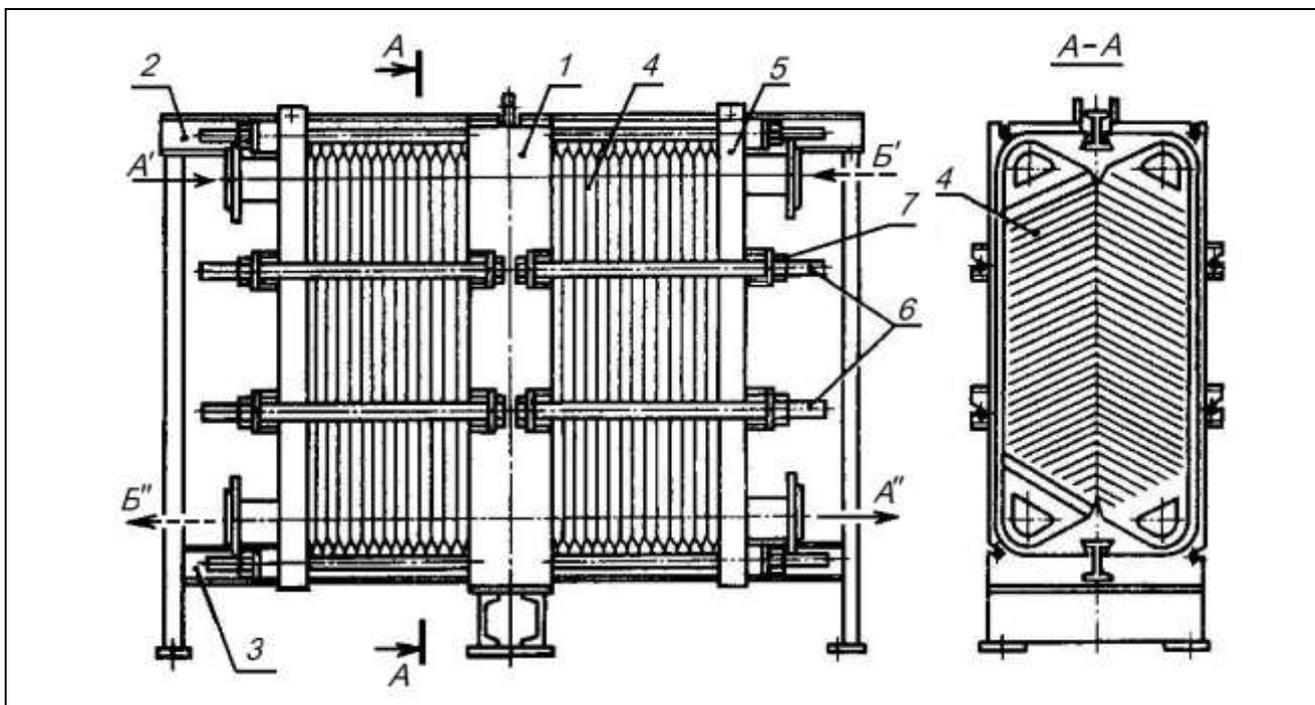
Разборный пластинчатый теплообменник (ТПР) на трехопорной раме (исполнение 3): 1 – центральная неподвижная плита; 2 – верхняя, 3 – нижняя штанги; 4 – пакет пластин; 5 – подвижная нажимная плита; 6 – болт-стяжка с резьбой; 7 – гайка
